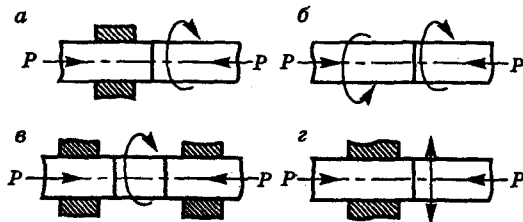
Принципиальная схема процесса сварки трением: а — сварка с вращением одной детали; б — сварка с вращением двух деталей; в — одновременная сварка трех деталей; г — сварка вибротрением
